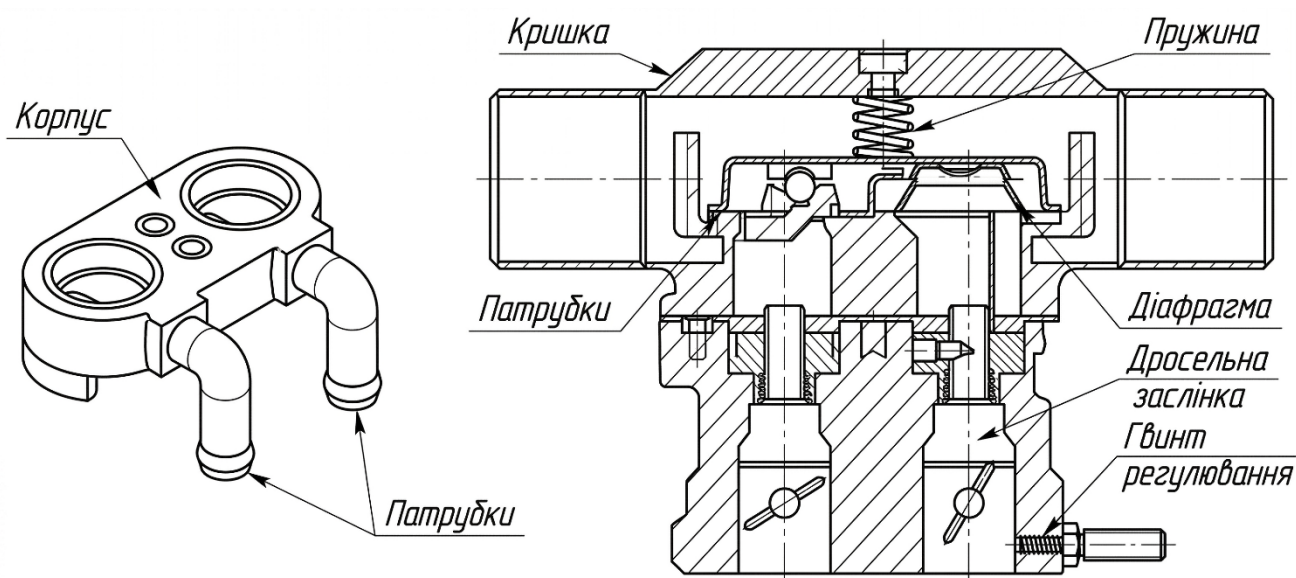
Загальний вигляд і схема двокамерного газового змішувача.
